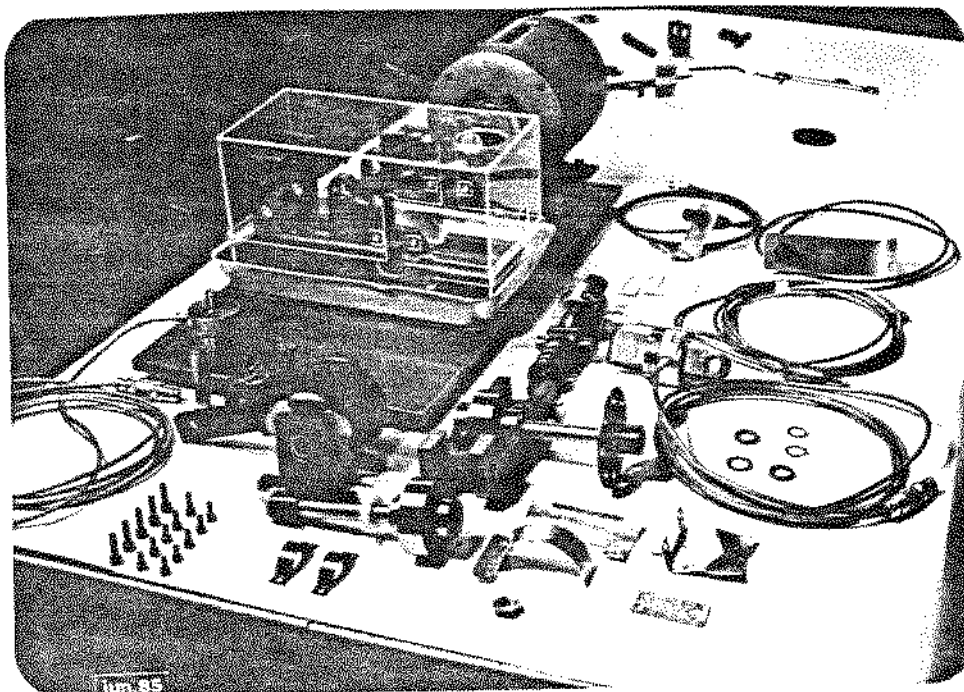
Montagem do motor, base e conjunto do freio da máquina de ensaios.
